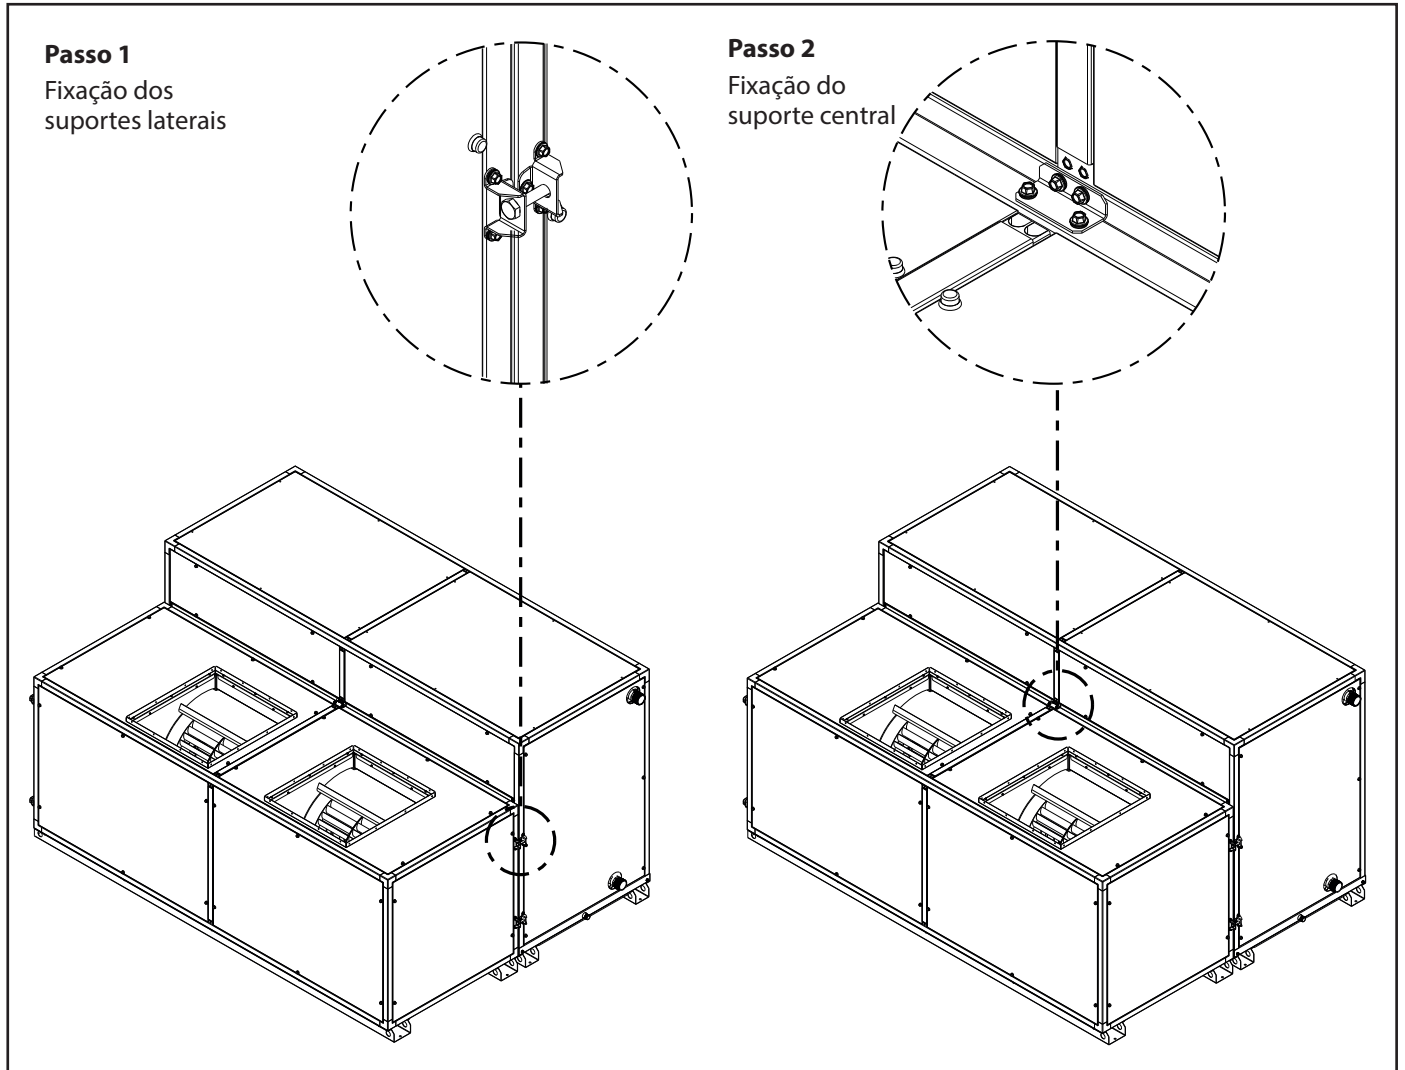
Detalhe de fixação dos módulos para montagem horizontal
